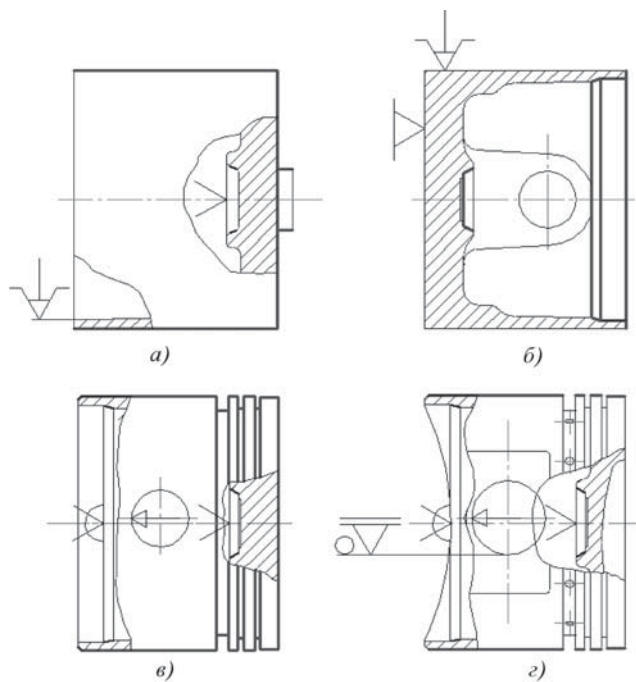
Схемы установки заготовки поршня при ее предварительной токарной обработке (а), расточке установочных конических отверстий (б), полустивовой обточке головки и юбки, прорезания канавок под поршневые кольца (в) и формирования овально-бочкообразного профиля поршня (г)
